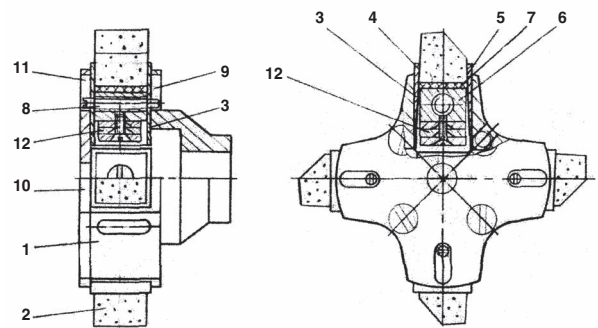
Сборный абразивный инструмент с радиально-подвижными сегментами для внутреннего шлифования: 1 — корпус; 2 — абразивный сегмент; 3 — обойма; 4, 5 — наклонные боковые участки абразивных сегментов; 6 — фиксатор; 7 — прокладка; 8 — ось фиксатора; 9 — паз корпуса; 10 — крышка; 11 — паз крышки; 12 — груз.
